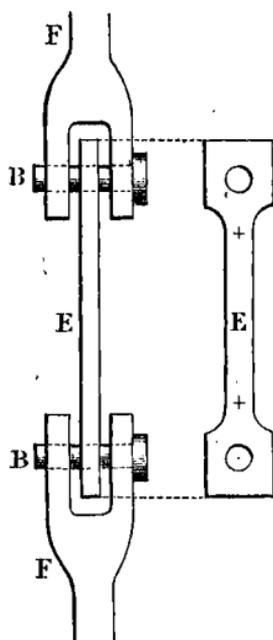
Mode d'attache des éprouvettes pour câbles.
